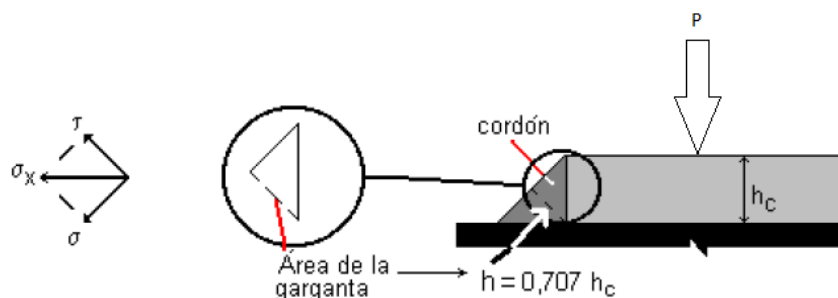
Nomenclatura para cordón de soldadura
